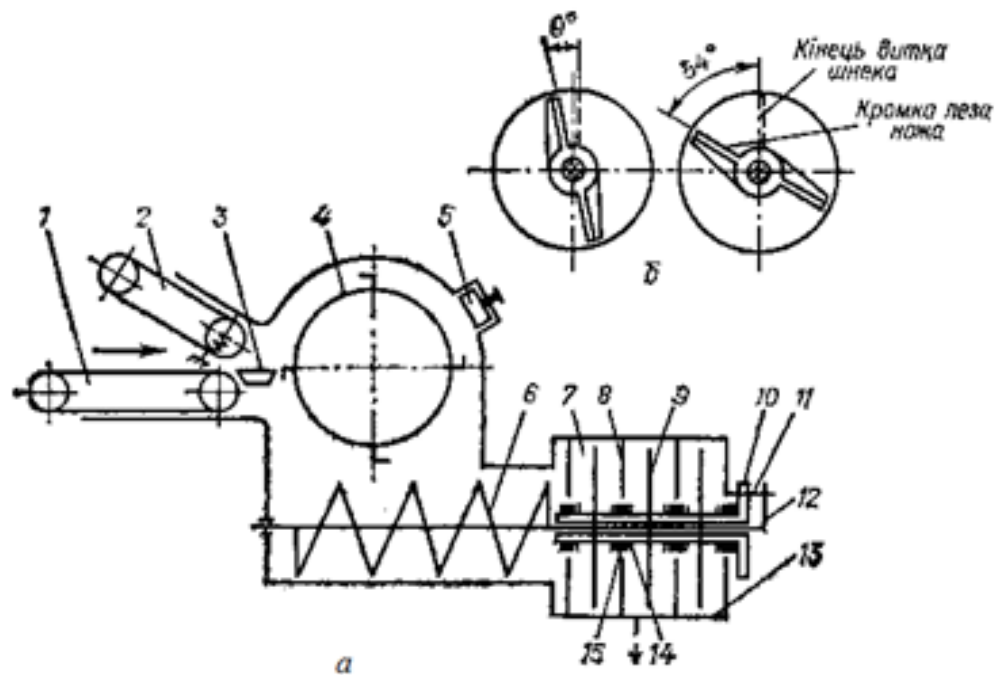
Конструктивно-функціональна схема (а) і схема регулювання ступеня подрібнення продукту (б) подрібнювача ІКВ-5А «Волгарь-5»; 1 - подавальний транспортер; 2 - транспортер пресувальний; 3 - пластина протиризальна; 4 - барабан ножовий; 5 - пристрій заточувальний; 6 - шнек; 7 – апарат вторинного різання; 8 - нерухомий ніж; 9 - ніж рухомий; 10 - втулка; 11 - зрізний штифт; 12 - фланець вала шнека; 13 - опора нерухомих ножів; 14 - прокладка; 15 – кільце» [7].
